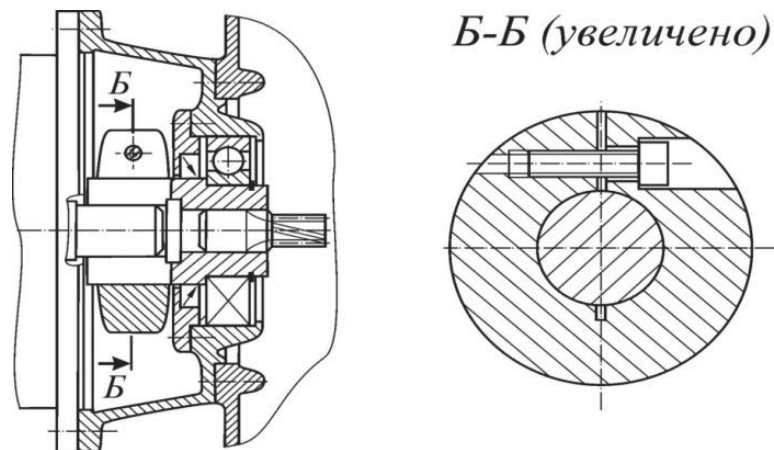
Трехопорный вал (опоры вала двигателя не показаны) с шестерней, расположенной консольно
